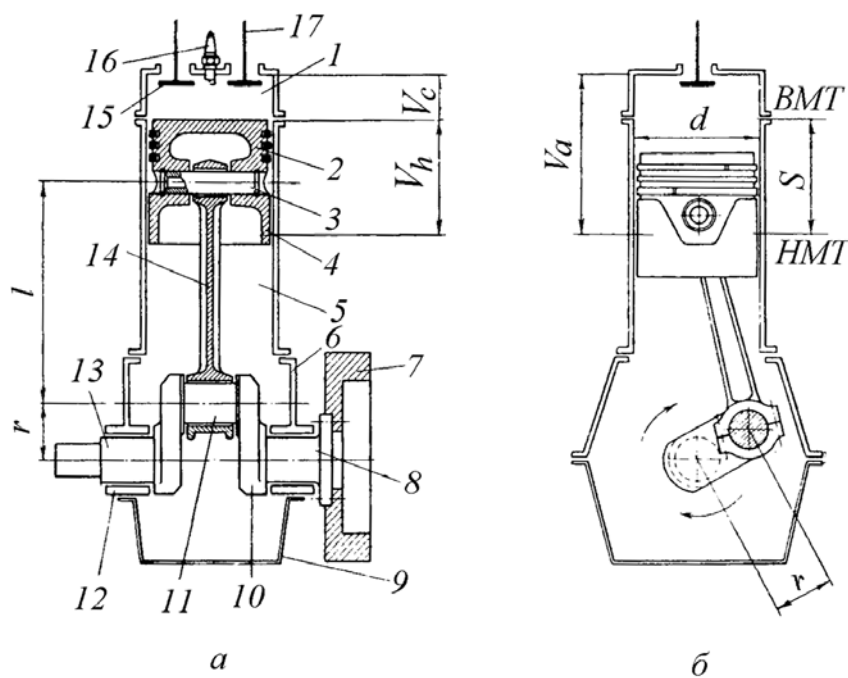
Схема устройства типичного поршневого двигателя внутреннего сгорания:
